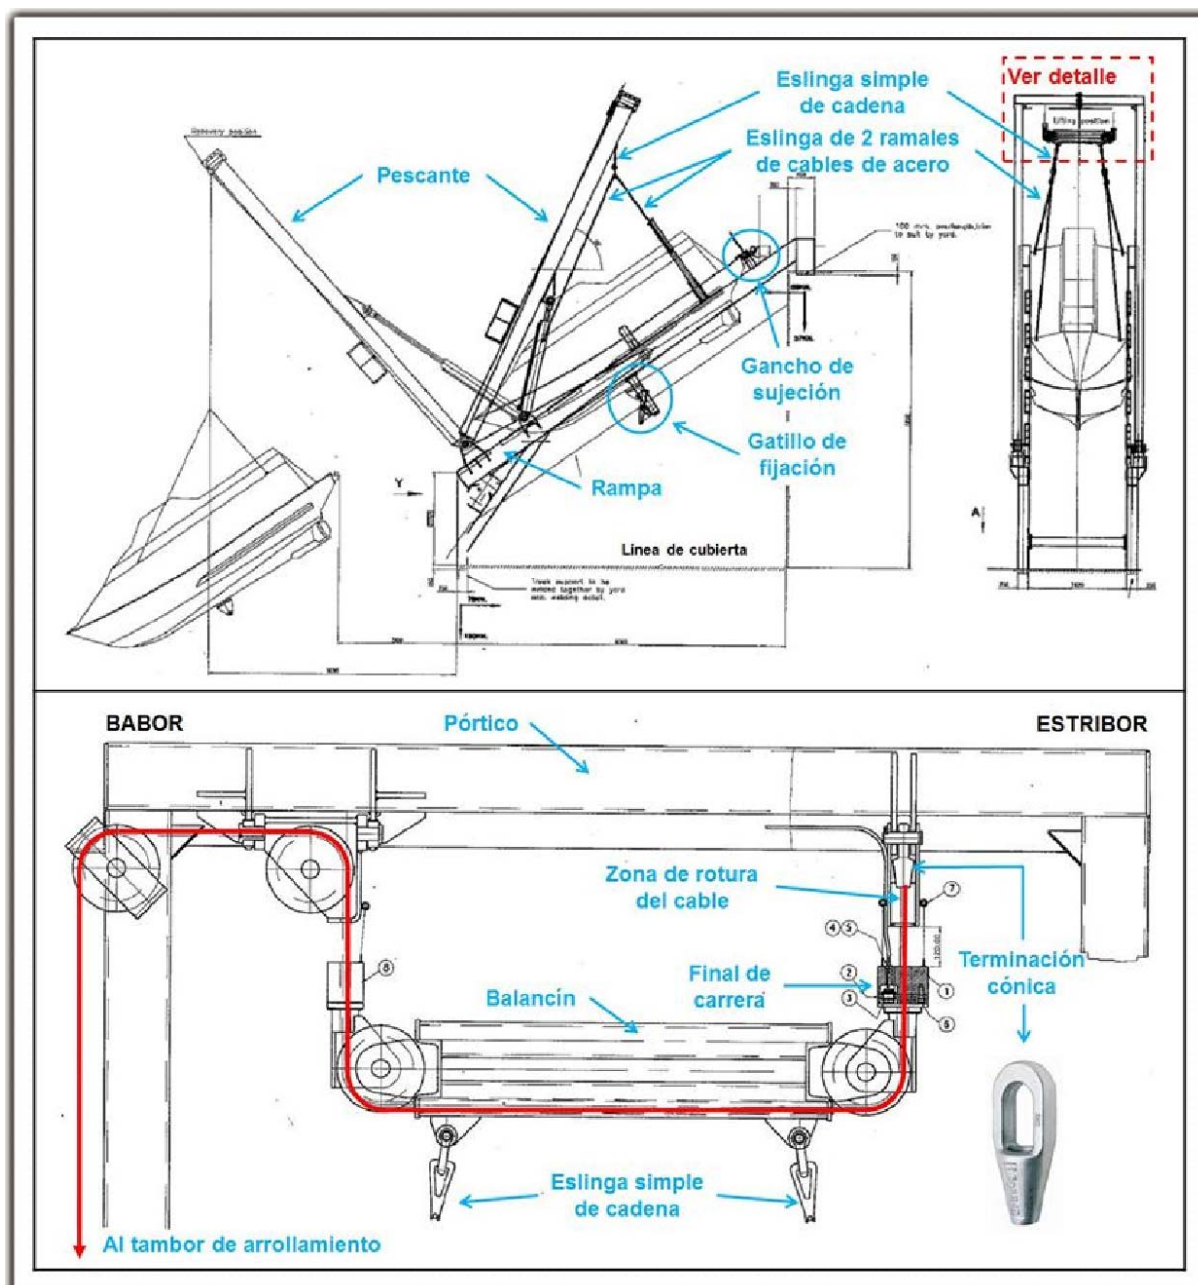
Disposición general del sistema de arriado del bote salvavidas mediante cables y detalle de la parte superior del pescante
